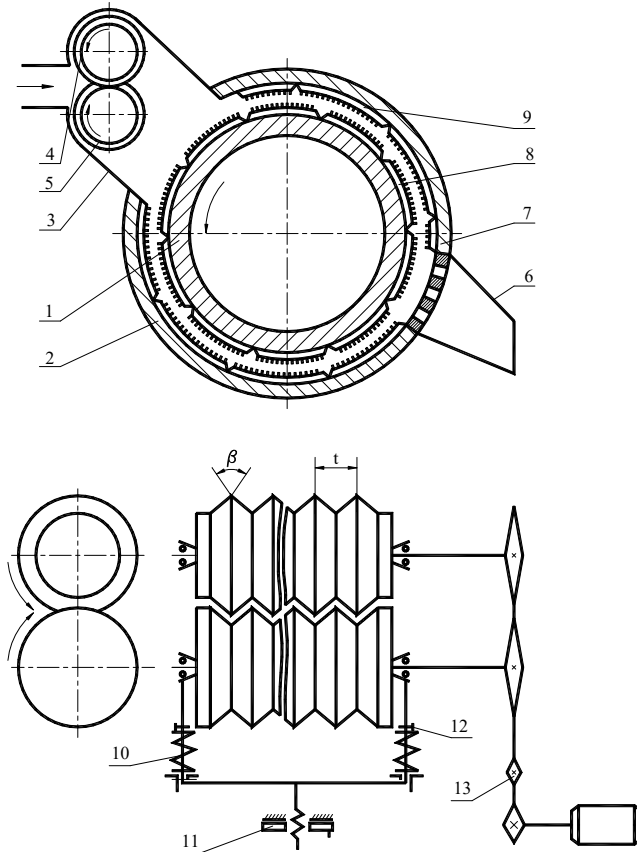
Схема технологічного валкового пристрою прохідного типу, що реалізує ослаблення структури натуральних шкір розтяганням і стиском: 1 – швидкообертвовий ротор; 2 – нерухомий корпус (барабан); 3 – завантажувальний патрубок; 4, 5 – живильні валки; 6 – розвантажувальний патрубок; 7 – робоча сітка; 8, 9 – планки з голкоподібною гарнітурою; 10 – торсіон; 11, 12 – механізми для регулювання зазора і зусилля притиснення валків; 13 – ланцюговий привід
